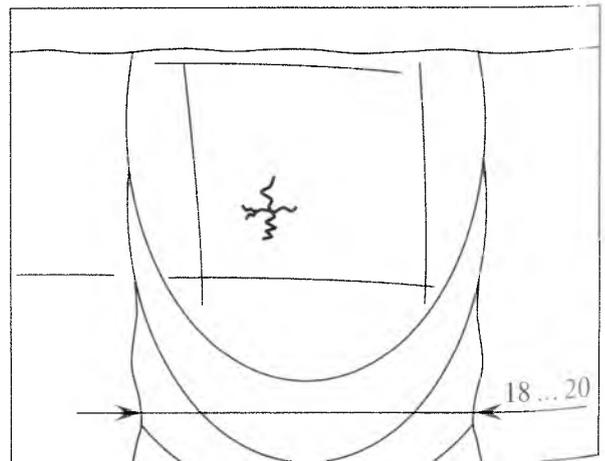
Звездообразная трещина (радиальная трещина) – трещины разного направления, исходящие из одной точки, – в сварном соединении лакирующего слоя на внутренней поверхности обечайки сосуда. Ширина сварного шва 18...20 мм
